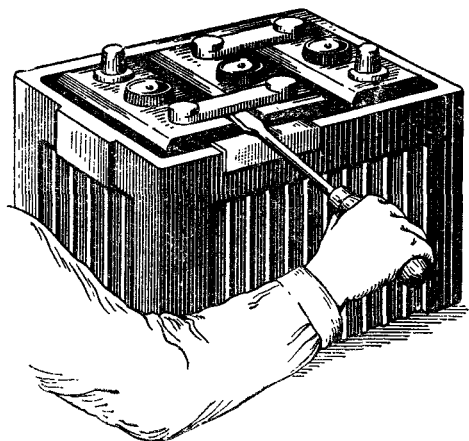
Проверка прочности сварки соединения перемычки со штырем баретки
